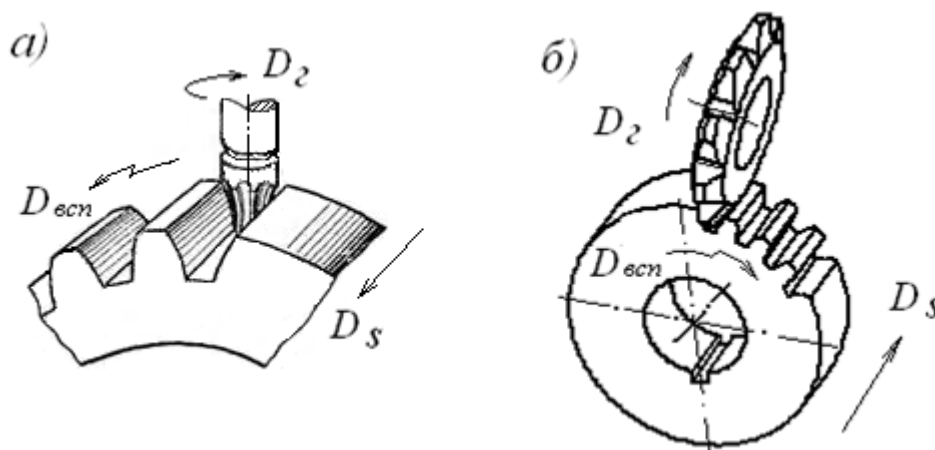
Схемы обработки венцов зубчатых колёс методом копирования
